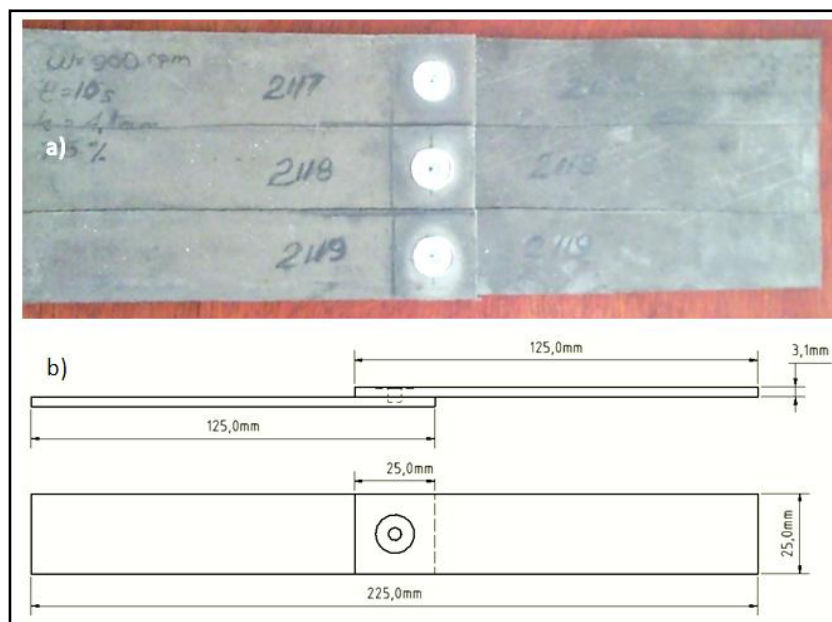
Soldadura por fricción agitación de punto, a) láminas base soldadas, b) esquema de las probetas objeto de estudio.
